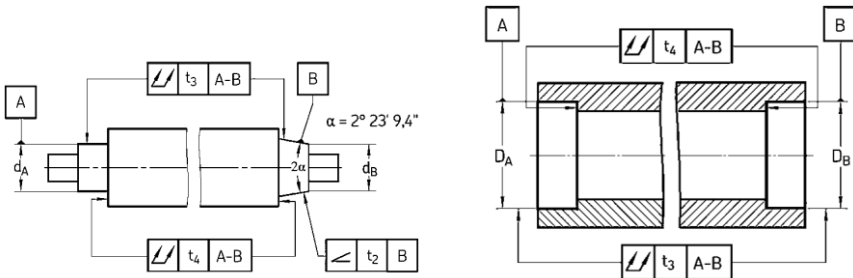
Відхилення форми місць під прецизійні підшипники на валу і в корпусі [31]
